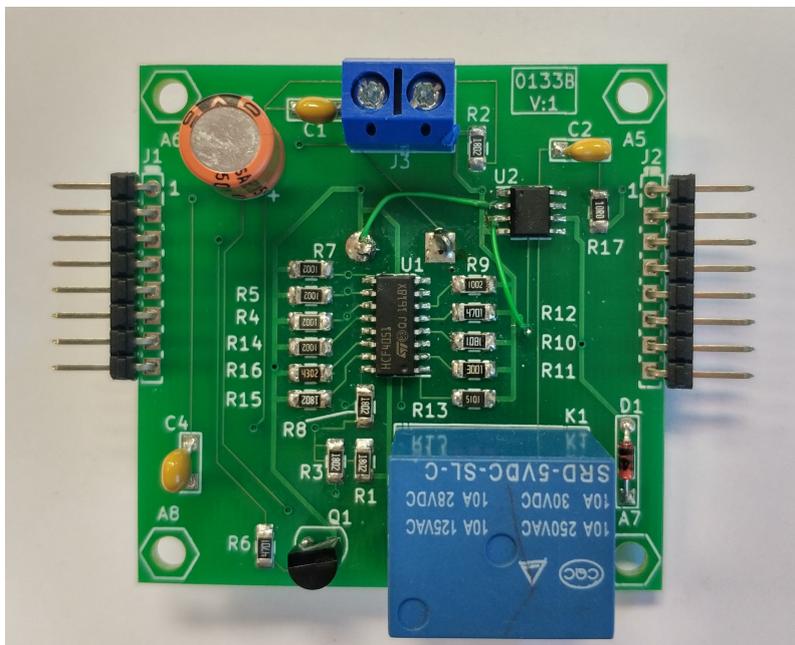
Montaje de la cara BOTTOM del Módulo de Audio.
